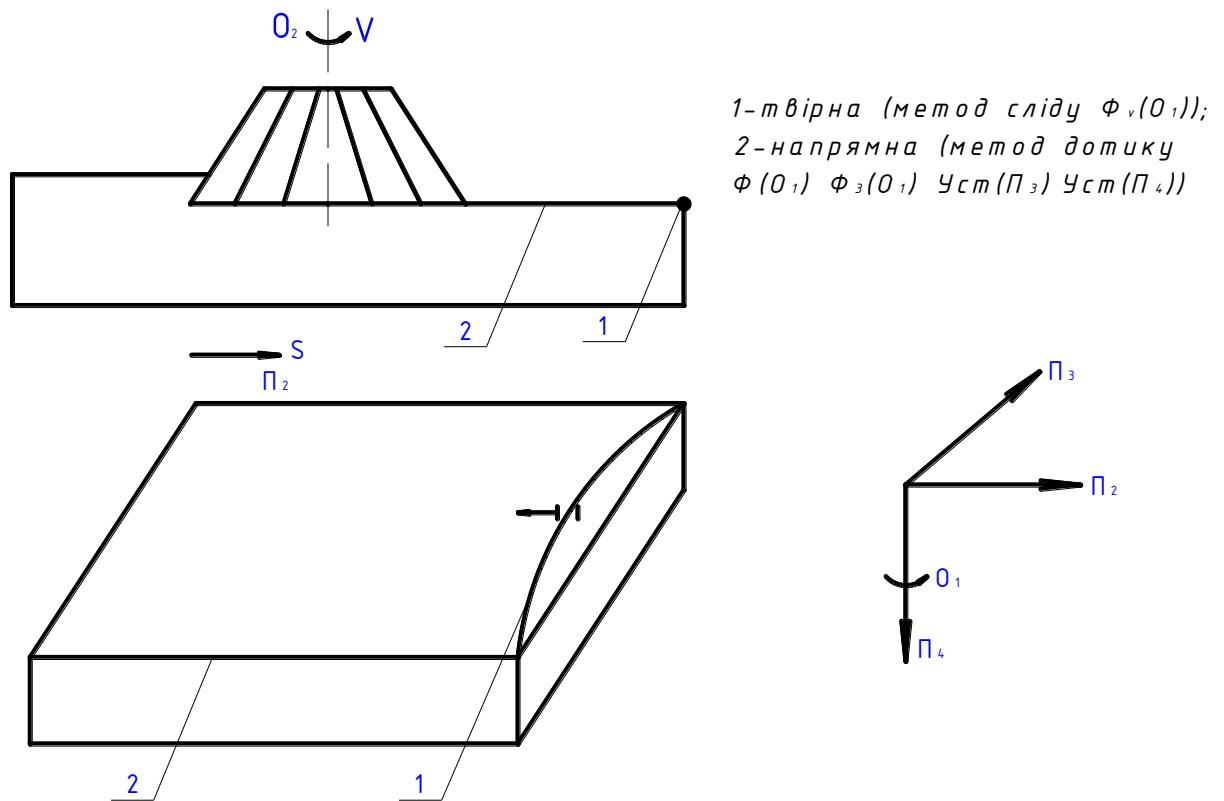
Рух інструменту при фрезеруванні торцевою фрезою.
